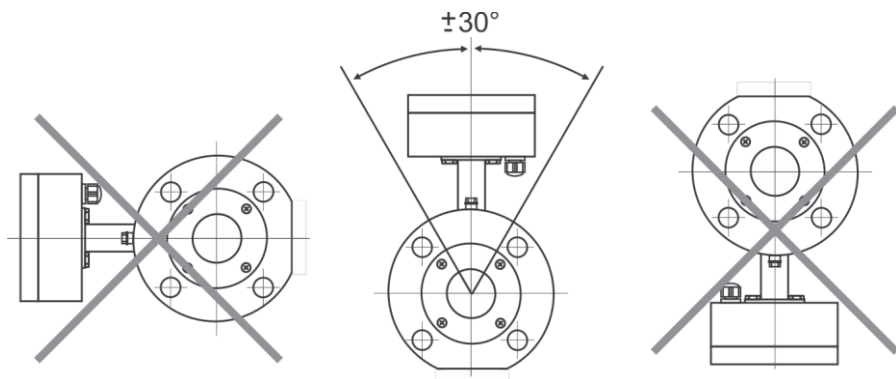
Допускаемая ориентация расходомера при установке в горизонтальные и наклонные трубопроводы
